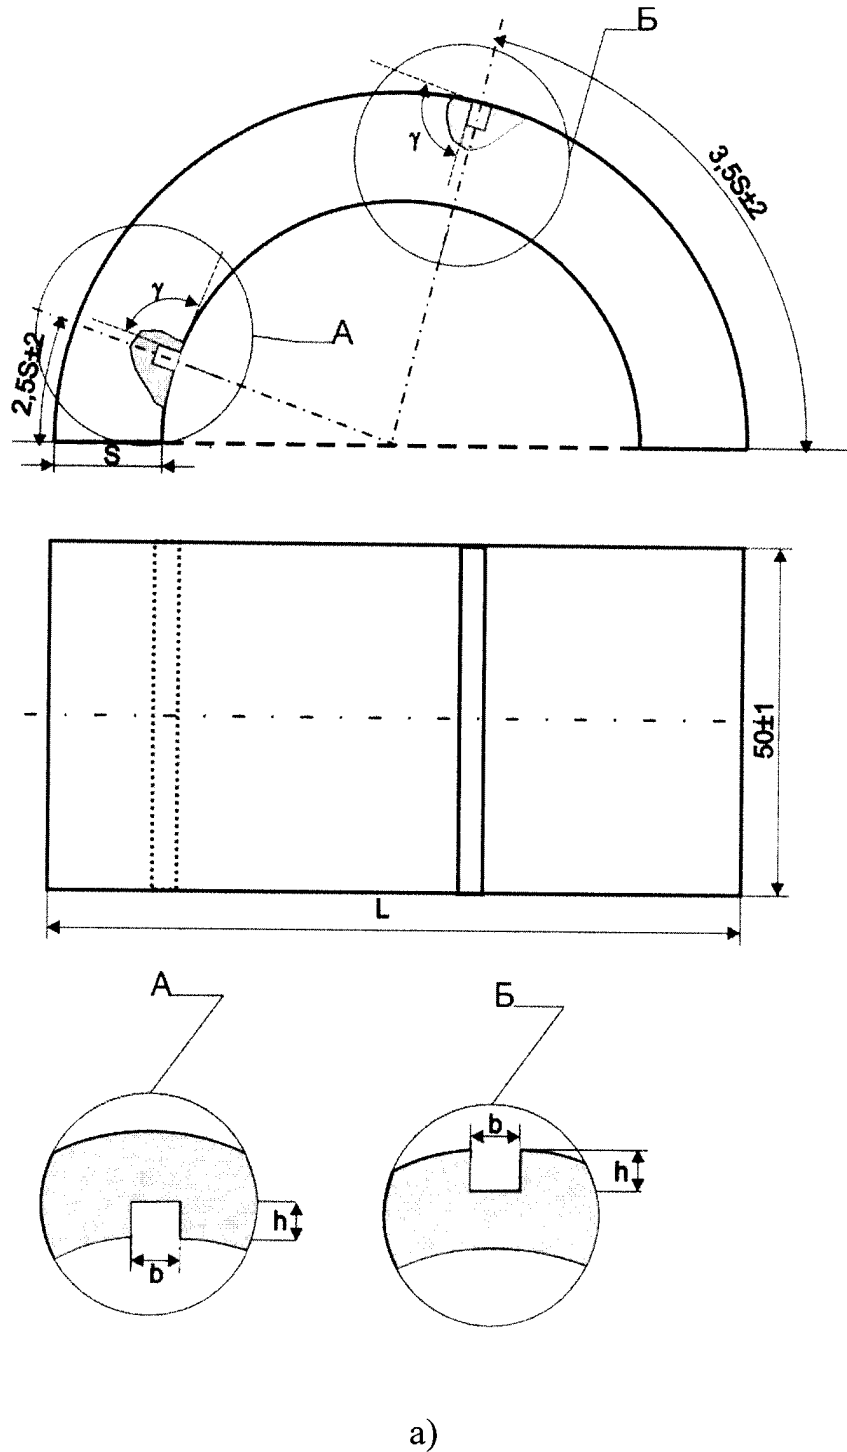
Стандартный образец предприятия с рисками для УЗК гибов труб
